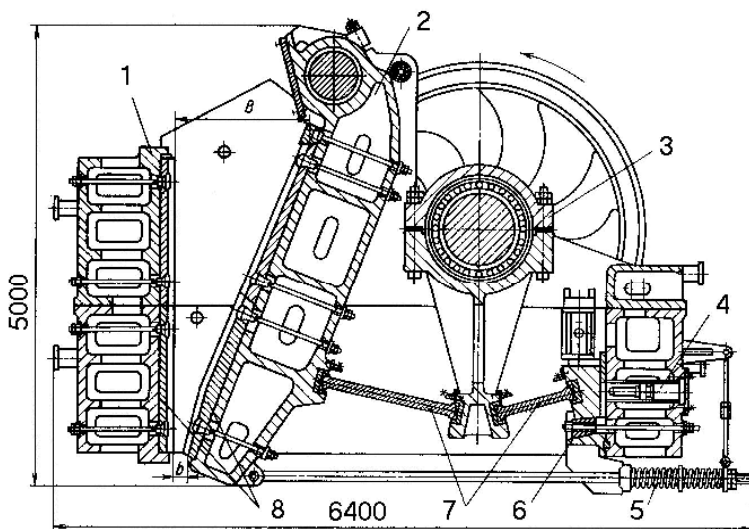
Щековая дробилка с простым движением щеки типа СМД
